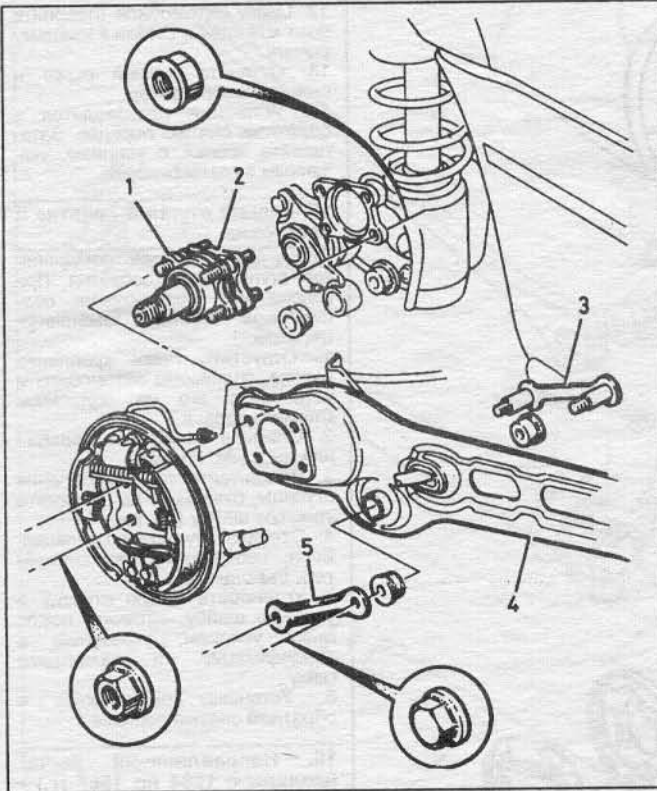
Сборка правого направляющего рычага и соответствующих компонентов: 1 - цапфа; 2 - подшипниковый узел; 3 - внутренний управляющий рычаг; 4 - направляющий рычаг; 5 - внешний управляющий рычаг.
